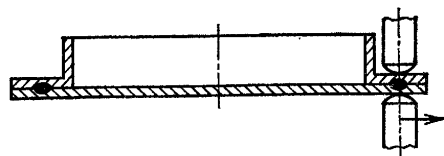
Схемы создания перемещений, противоположных сварочным
